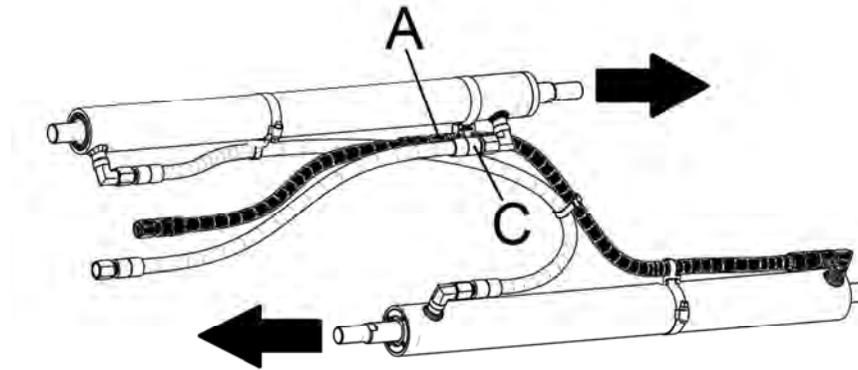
Impianto idraulico per versioni senza traslazione con posizione ingressi alimentazione forche centro telaio
